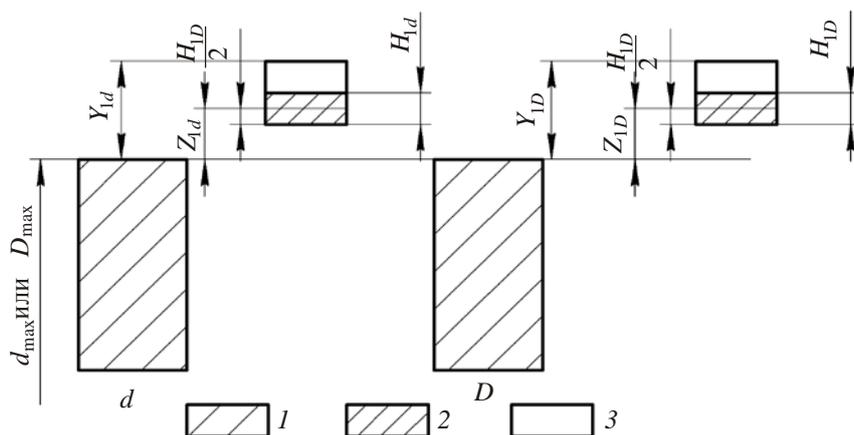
Схема расположения полей допусков калибров-колец для центрирующих диаметров d и D вала:
